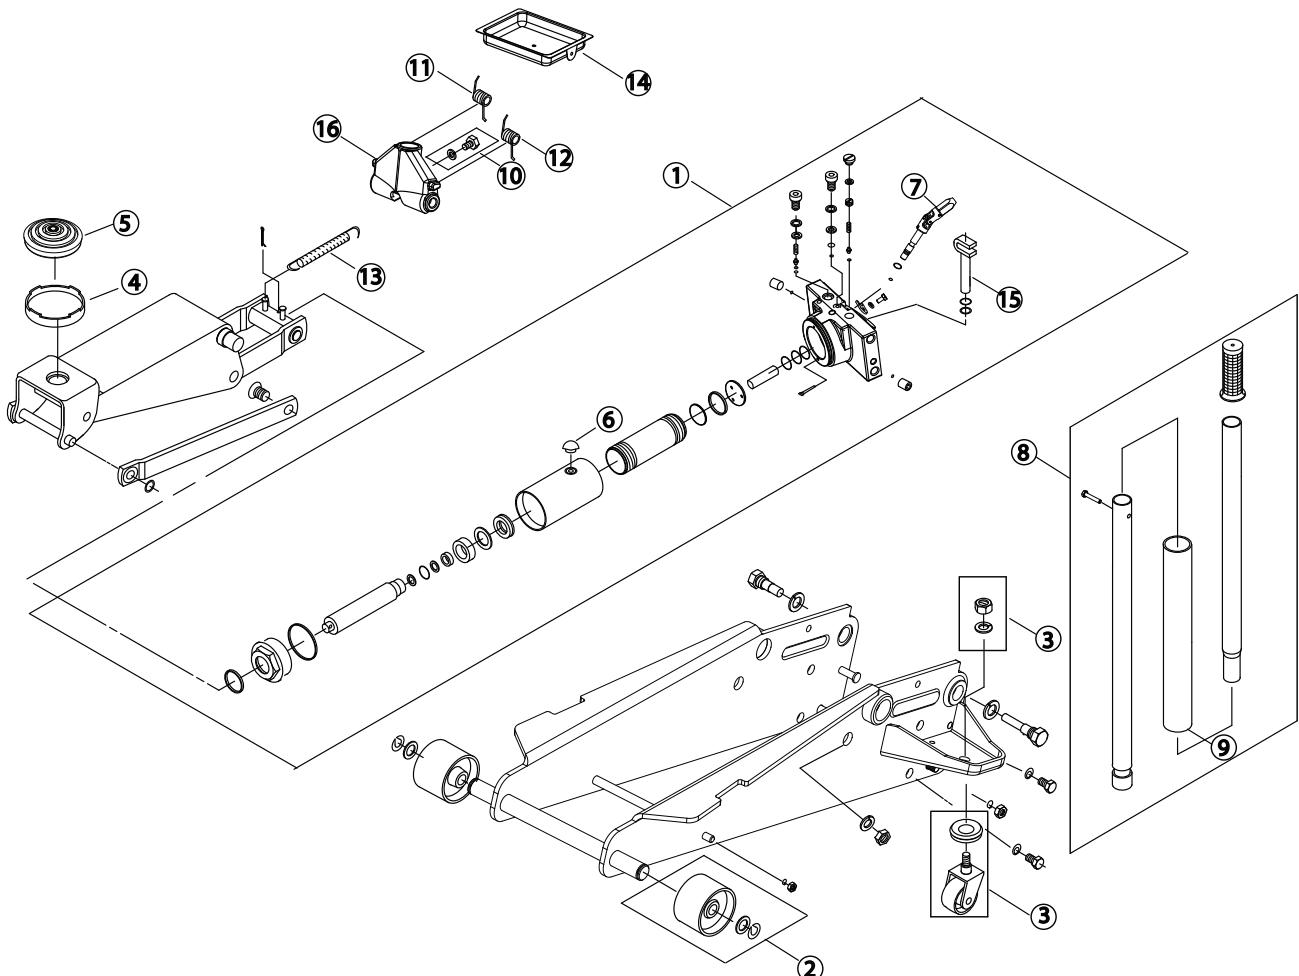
Ilustración de piezas de repuesto para el modelo G-737
